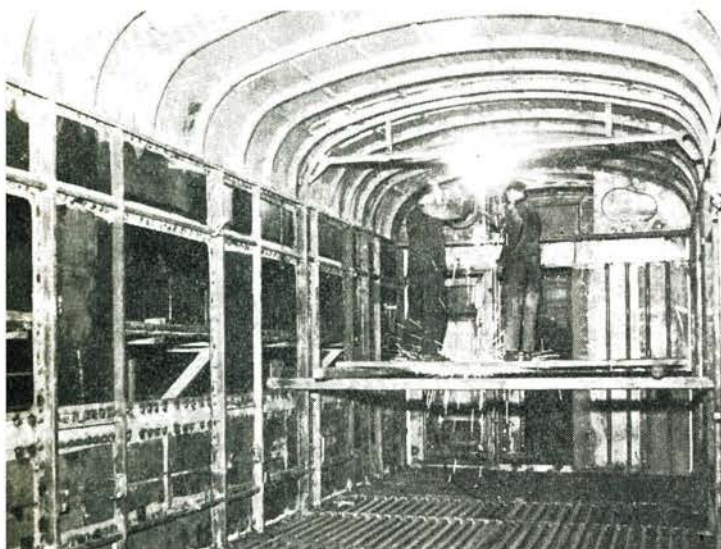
Schweißarbeiten an der Stirnwand eines Wagenkastens; deutlich sind die Punktschweißstellen der einzelnen Längswandbleche erkennbar
